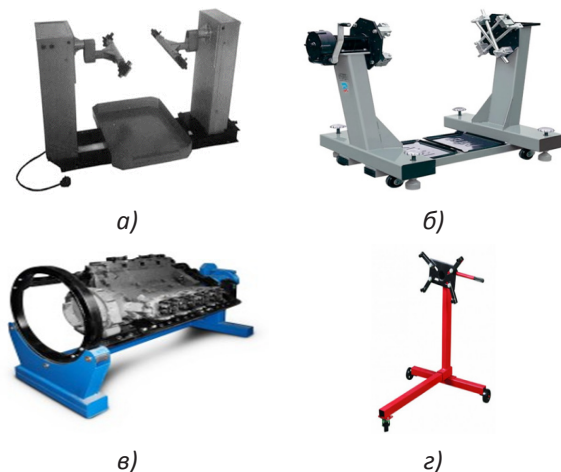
Стенд для разборки и сборки автомобильных двигателей:
